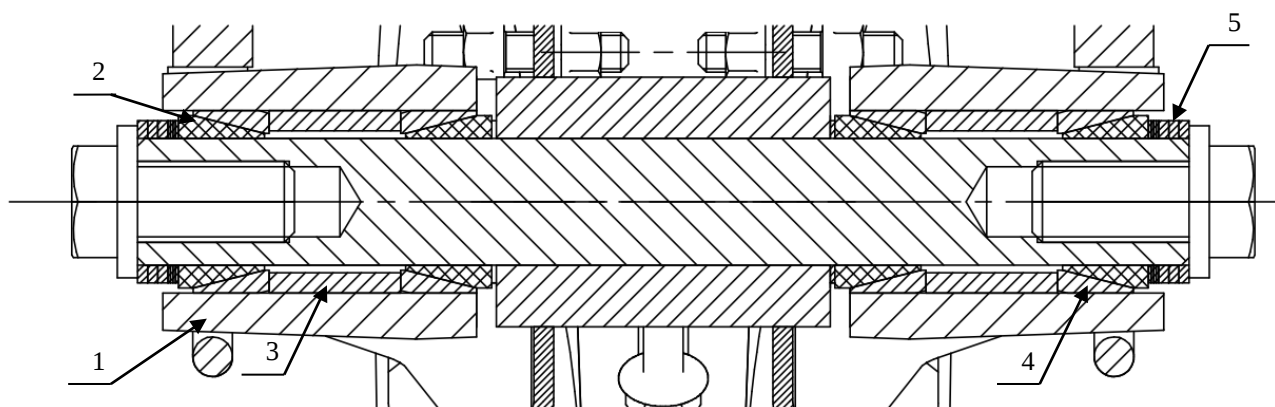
Конструкція трибоспрямижень із використанням конусних підшипників ковзання з композитних матеріалів: 1 – важіль; 2 – конусна втулка з композитного матеріалу; 3 – дистанційна втулка; 4 – втулка зі сталі для запресовування у важіль; 5 – регулювальні шайби
